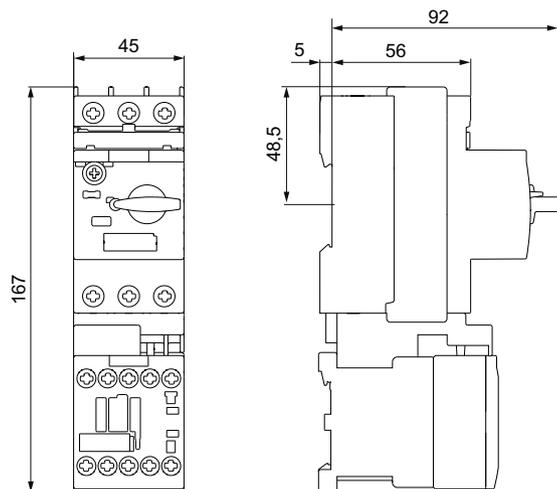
Arrancador directo S00, AC/DC, bornes de tornillo 3RA2110-..A
